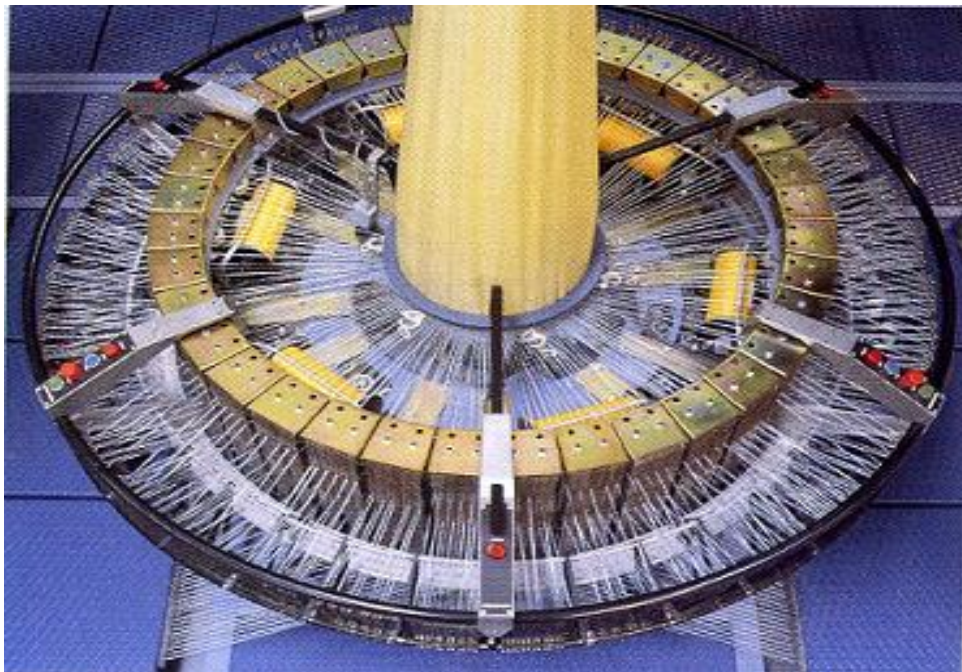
, MÁQUINA TEJEDORA CIRCULAR -VISTA AÉREA-
